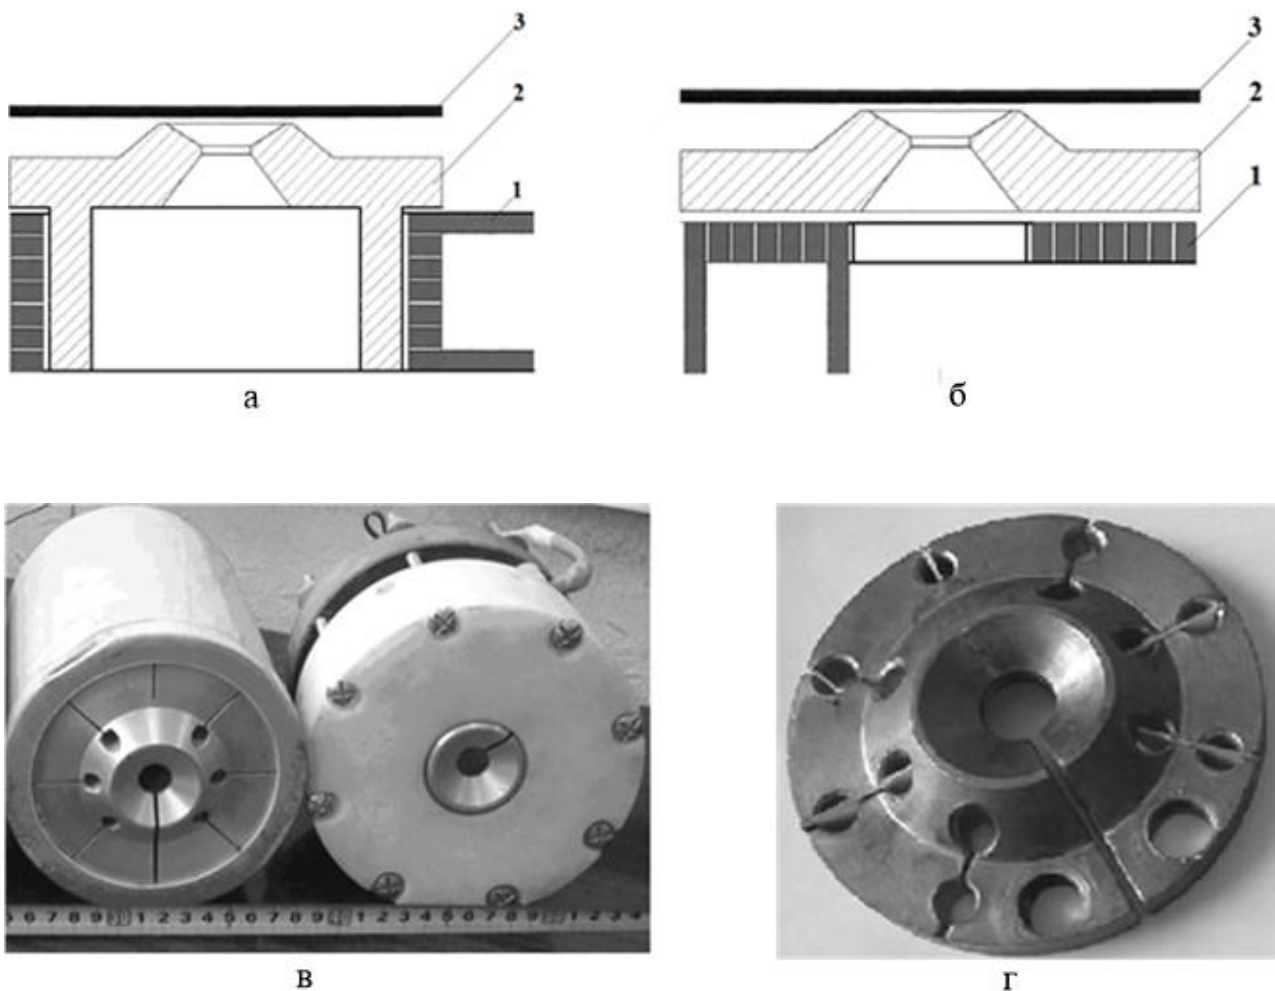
Узгоджувальний пристрій різного конструктивного виконання:
